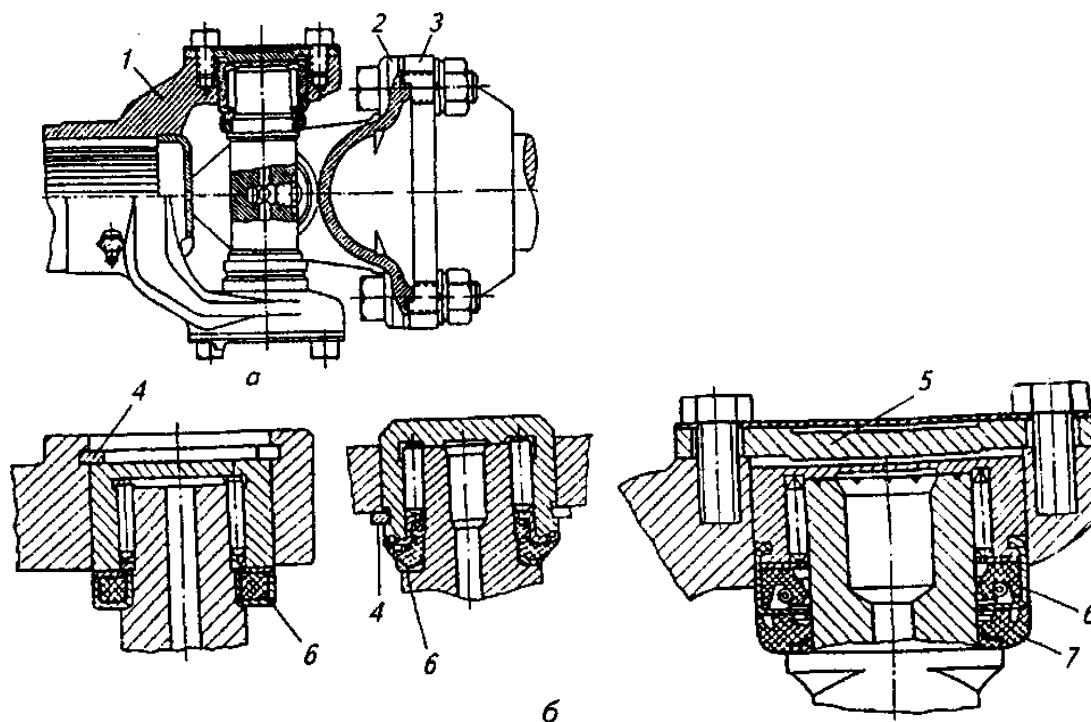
Вилки игольчатых карданов неравных угловых скоростей: а — вилка игольчатого кардана; б — варианты крепления стакана и уплотнения игольчатого подшипника; 1 — проушина вилки; 2, 3 — фланцы; 4 — стопорное кольцо; 5 — крышка; 6 — самоподжимной сальник; 7 — резиновый торцевой сальник
